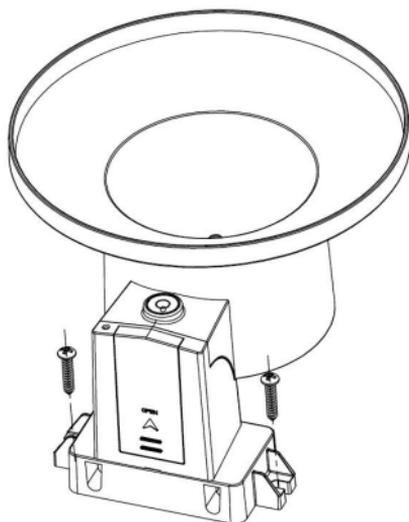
Diagramm zur Installation des Regenmessersensors mit Schrauben
